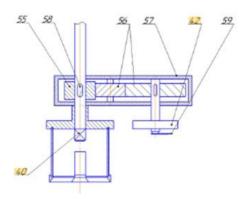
Механическая индикация положений регулируемого упора: 55 — шестеренка ведущая; 56 — шестеренки; 57 — корпус редуктора; 58 — циферблат
